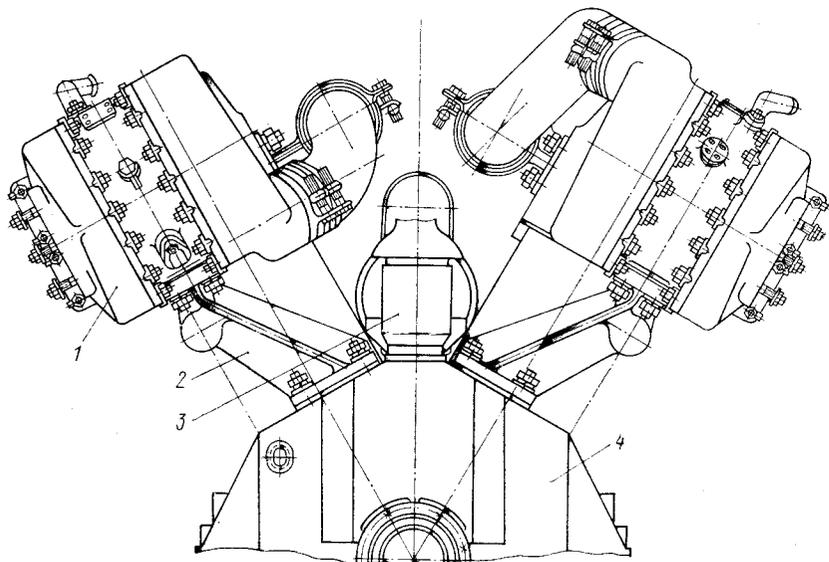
Установка турбокомпрессоров на дизель В2-800 ТК-С3:
